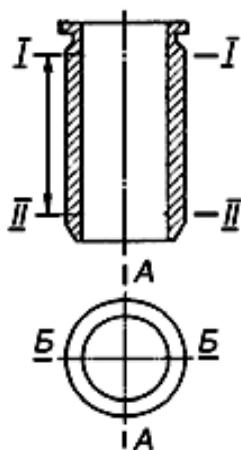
Схема замеров отверстия гильзы цилиндра (цилиндра в блоке):
